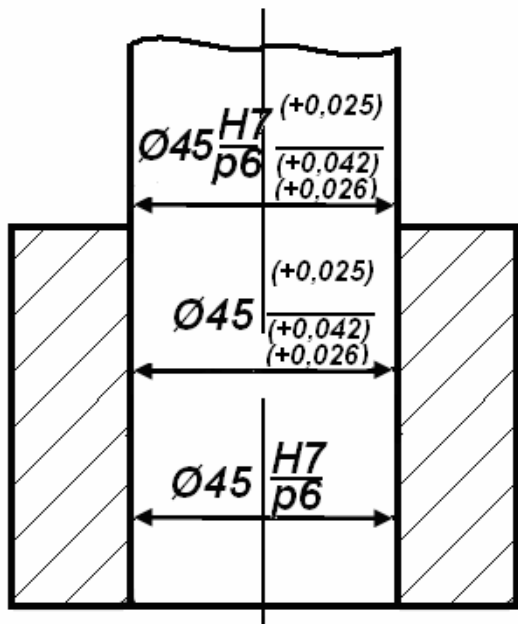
Примеры обозначения полей допусков и посадок на чертежах
